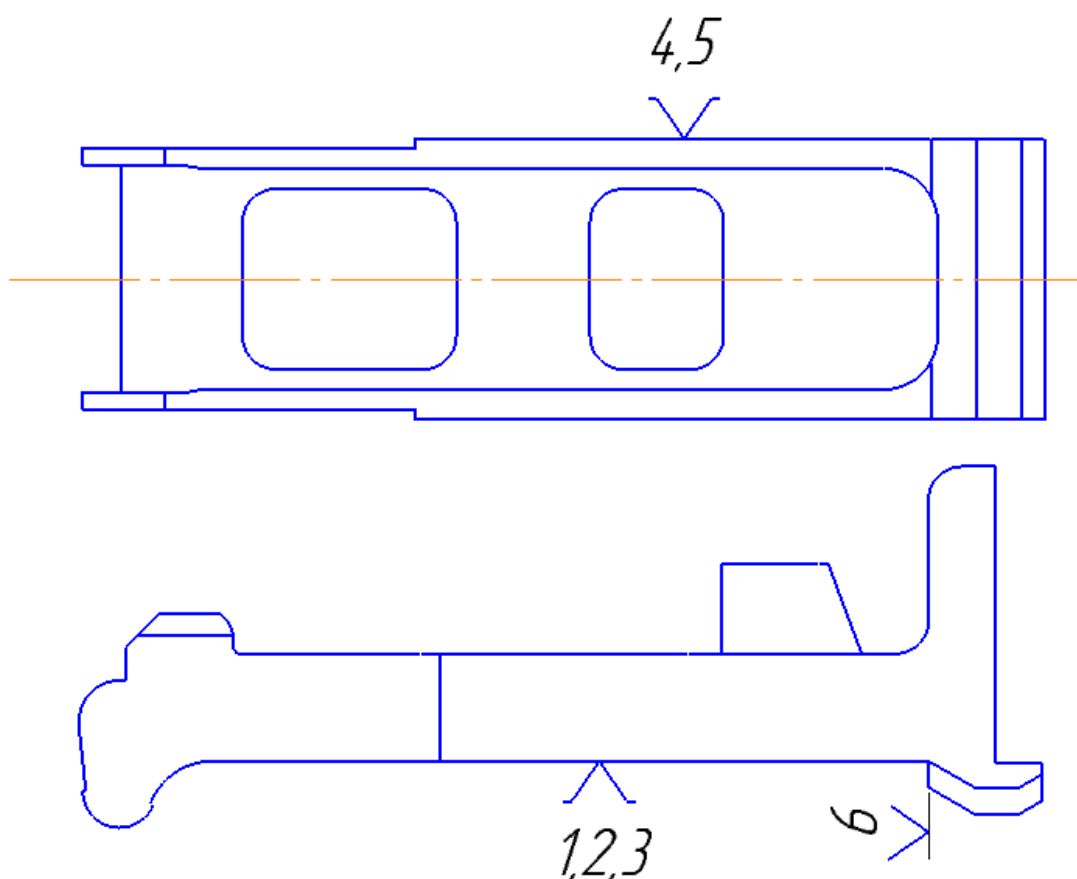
Схема базирования на операции 05. Фрезерная с ЧПУ
